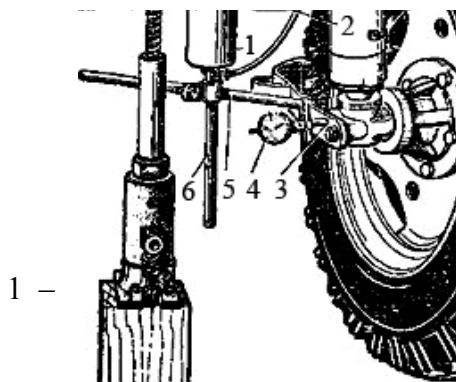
Перевірка радіального зазору в sprzęженні поворотна цапфа – втулка: електромагніт; 2 – передня вісь машини; 3 - шток; 4 – індикаторна головка; 5 – штатив; 6 – стійка.
